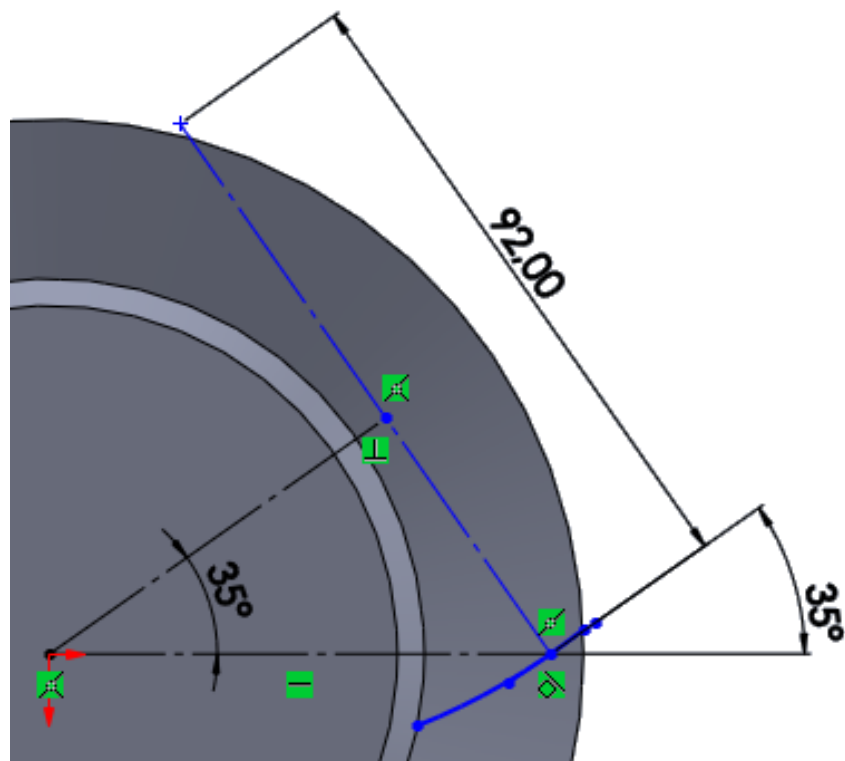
Método FaceMilling en CAD. Fuente Autor.
